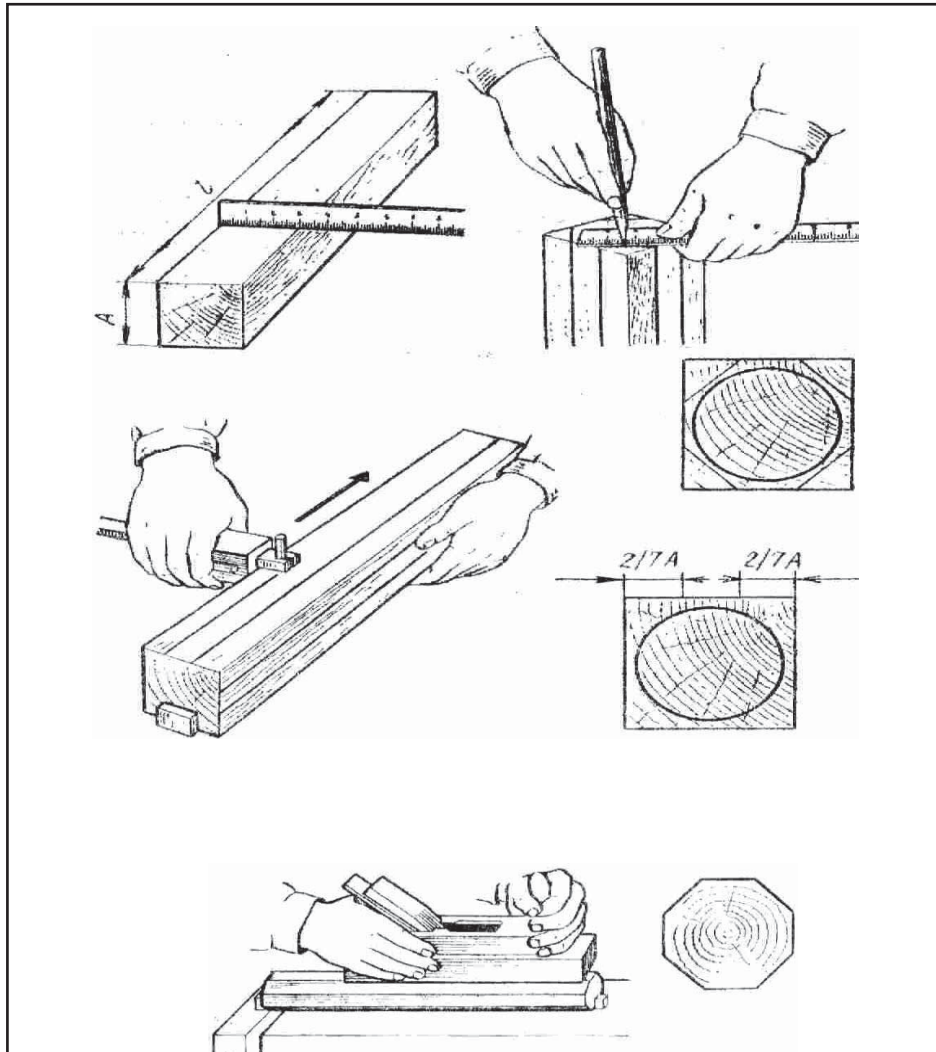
Підготовка дерев'яної заготовки до точіння
